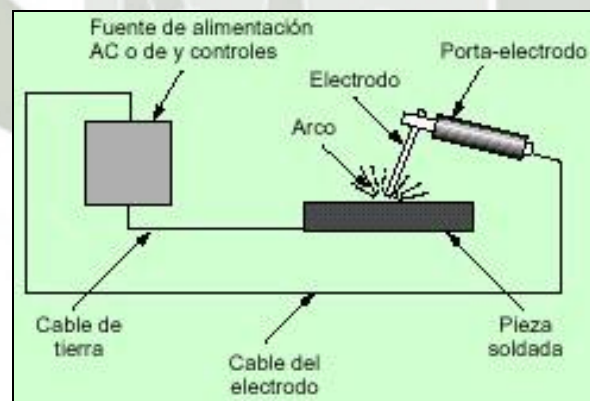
Esquema del proceso de soldadura eléctrica al arco
